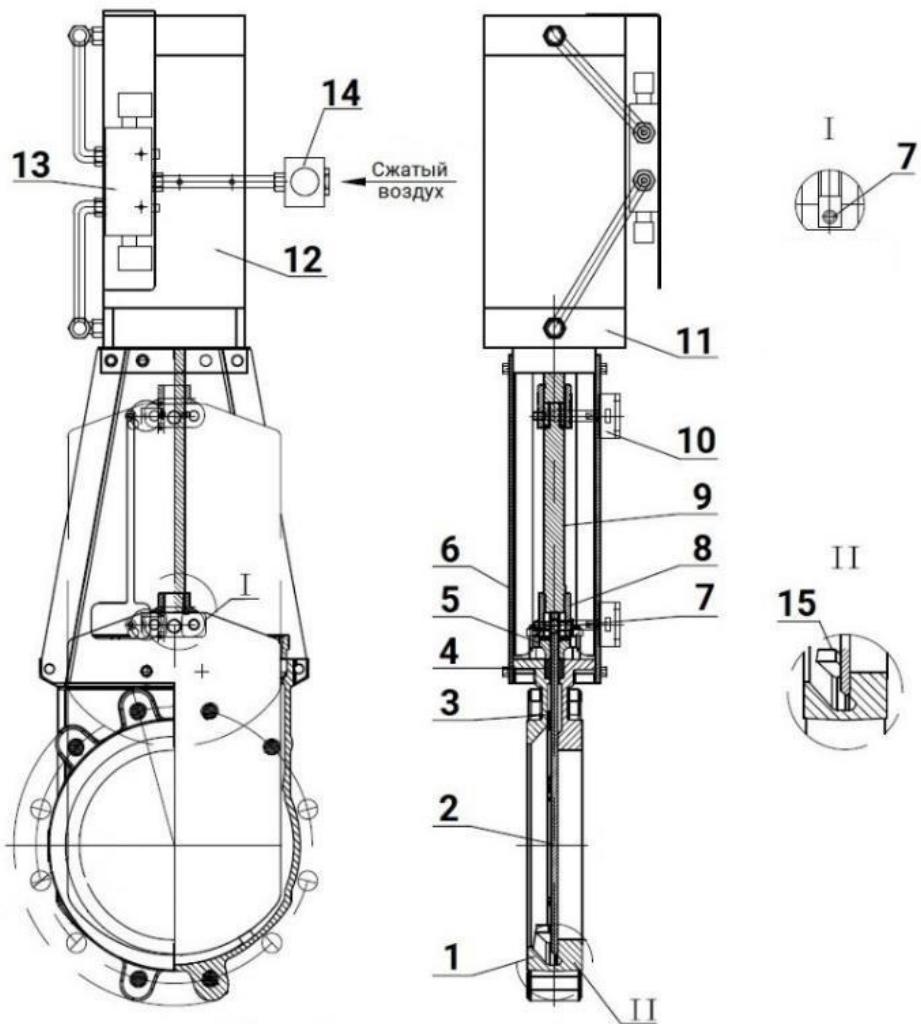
Деталировка задвижки в сборе с пневмоцилиндром
